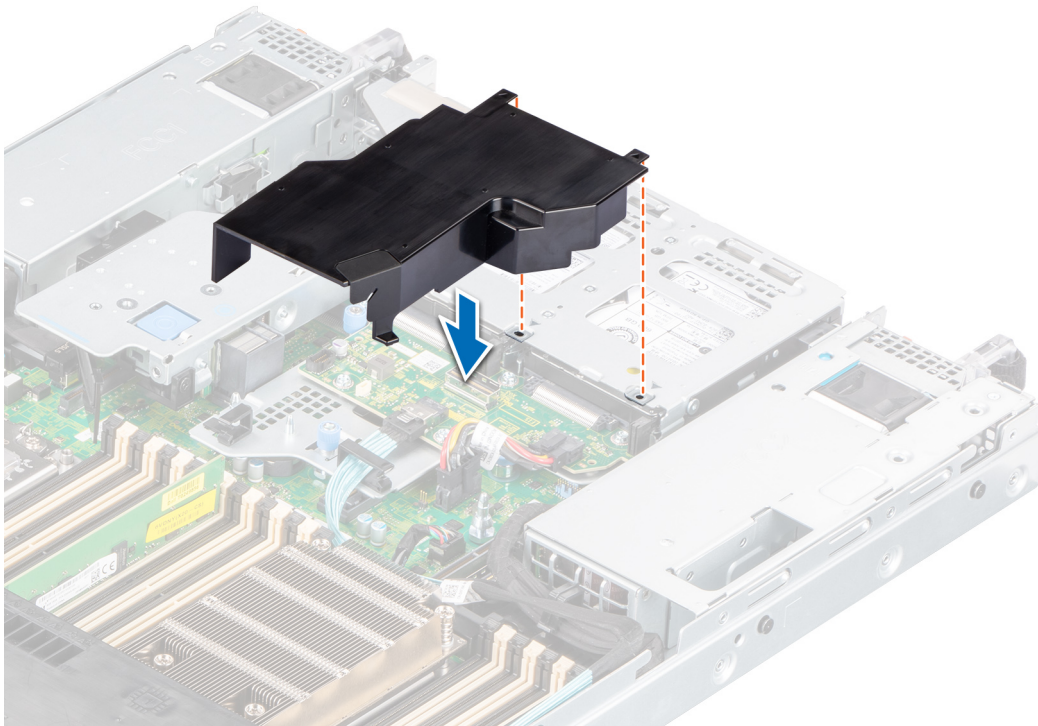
Einbauen des Kühlgehäuses auf das hintere Laufwerksmodul
